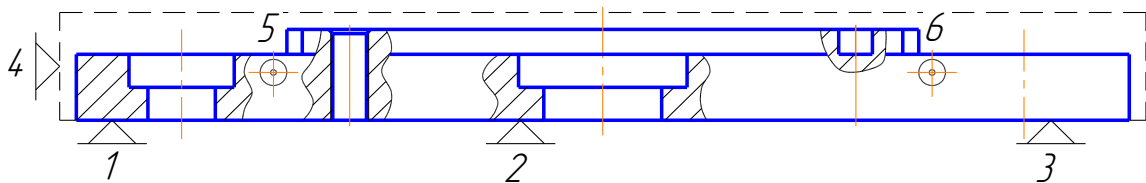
Схема базування заготовки під час її механічної обробки
